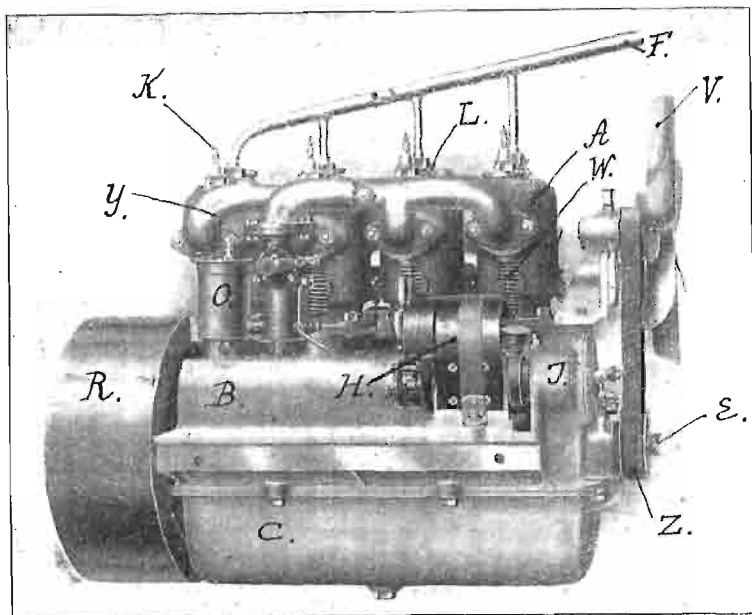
przedstawia silnik 4-cylindrowy firmy paryskiej: „Automobiles-Cornilleau“ 75 średnicy i 130 skoku. Cylindry odlane wspólnie. Chłodzenie na zasadzie samoczynnego krąże-
